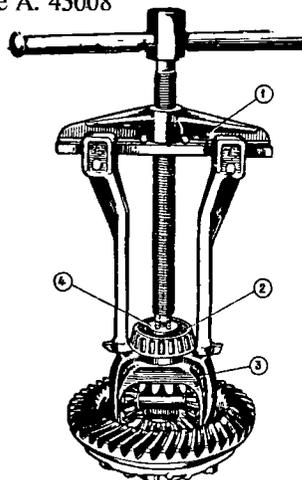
Снятие внутреннего кольца подшипника коробки дифференциала универсальным съемником А.40005/1/6: 1 - универсальный съемник А.40005/1/6; 2 - внутреннее кольцо подшипника; 3 - коробка дифференциала; 4 - упор А.45028
